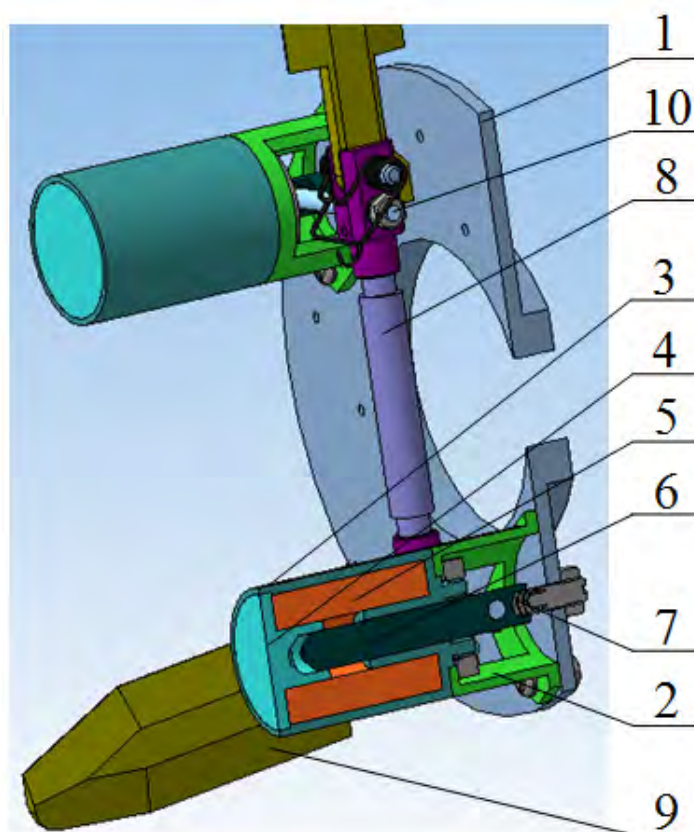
Конструктивно-компоновочная схема РП: 1 – корпус БПЛА; 2 – стойка; 3 – корпус ЭМ; 4 – стоп; 5 – обмотка; 6 – якорь; 7 – пружина; 8 – ось; 9 – руль; 10 – коромысло
